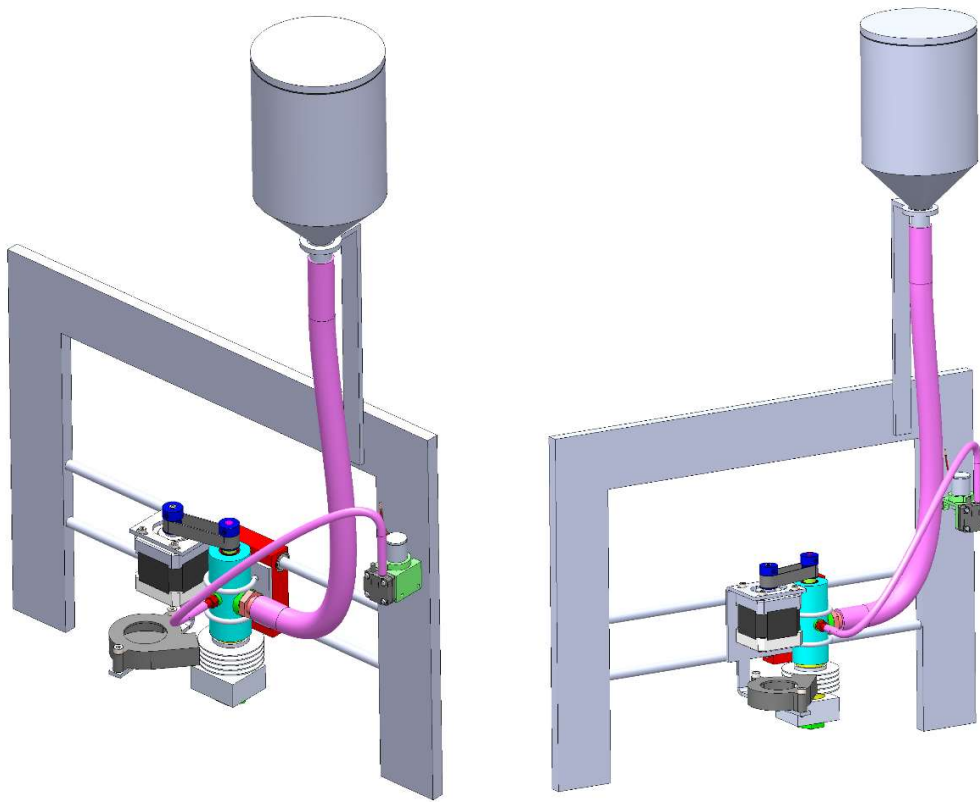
modelo final con bloque calefactor, disipador y ventilador incorporados
